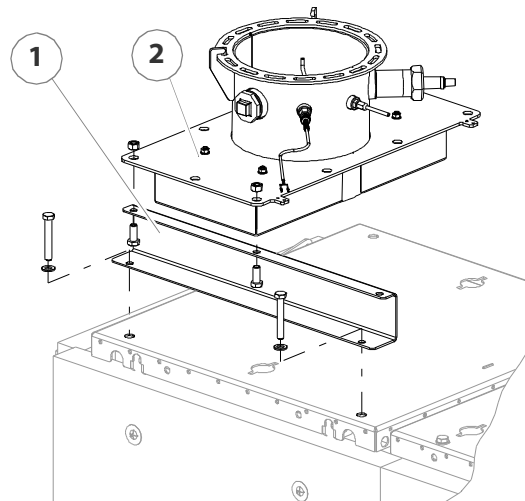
/11 - Démontage du carter d'échappement des gaz de combustion
